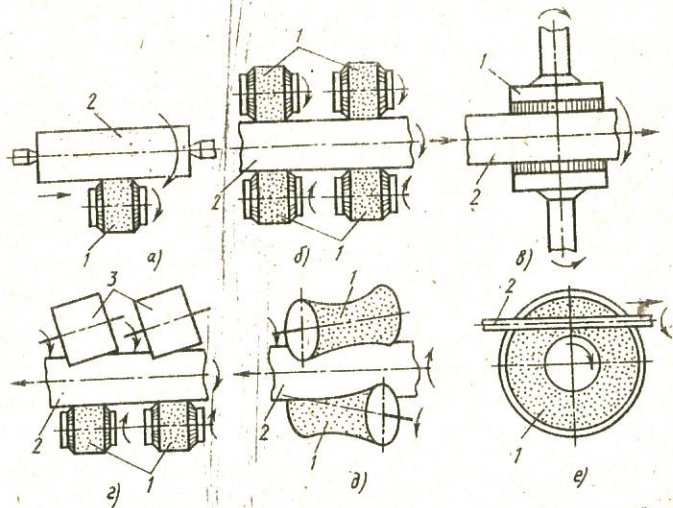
Схемы обработки на иглофрезерных станках моделей 6И9КС1110Ц (а), 6И9БС1123Ц (б), 6И9БР1122Т (в), 6И9БС2121Ц (г), 6И9БР2222Г (д), 6И9БС1210Т (е): 1 — иглофреза; 2 — заготовка; 3 — приводной ролик
